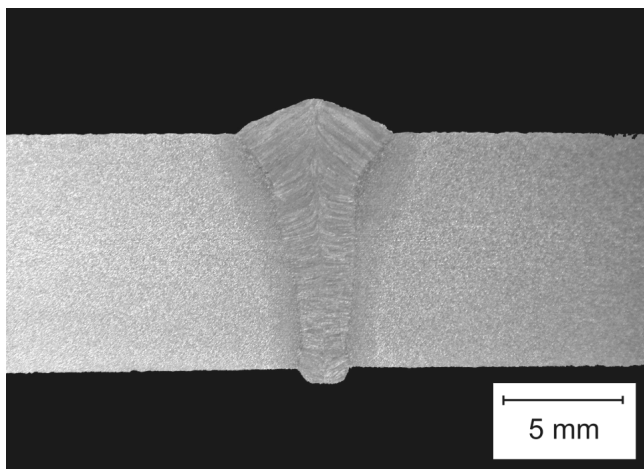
Traktorgeschweißte Stumpfnah 9 mm, 10 kW Laserleistung, 12 m/min Drahtvorschub, 2 m/min Schweißgeschwindigkeit
